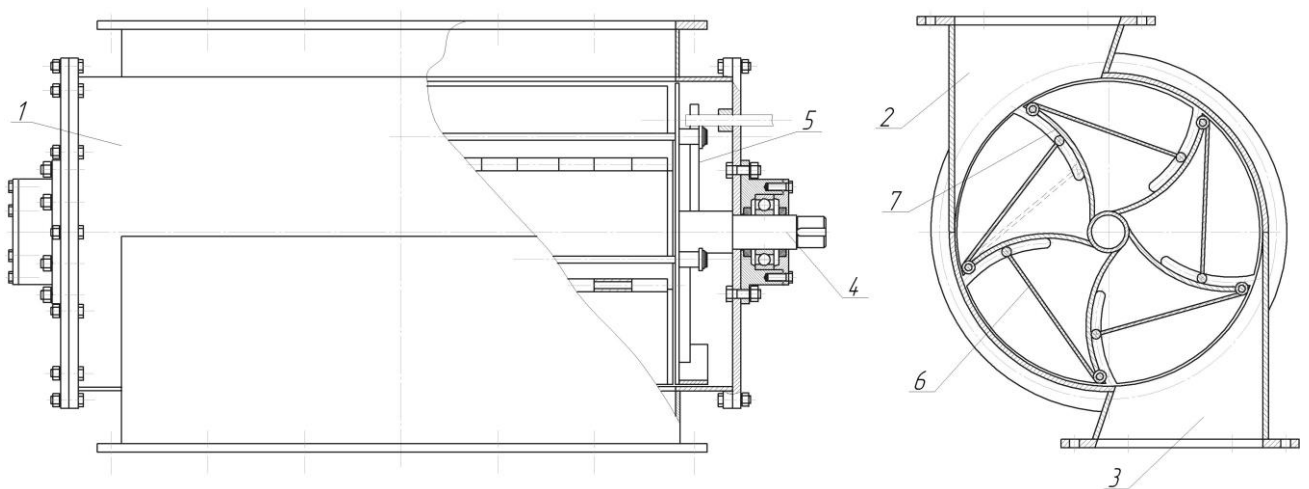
Розроблений барабанний дозатор із комірками змінного об'єму: 1 – корпус дозатора; 2 – вхідна горловина; 3 – вихідна горловина; 4 – приводний вал; 5 – копір; 6 – рухома лопатка; 7 – нерухома лопатка
